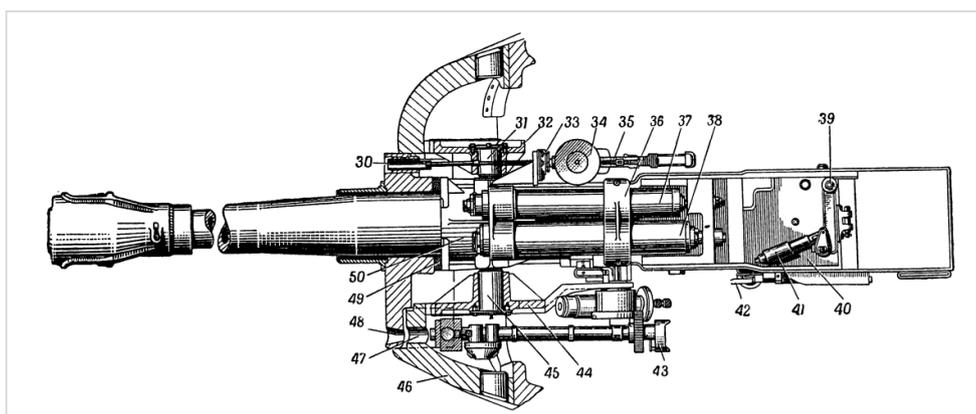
Установка пушки Д-25Т и спаренного с ней пулемёта (вид сверху) [7]:
